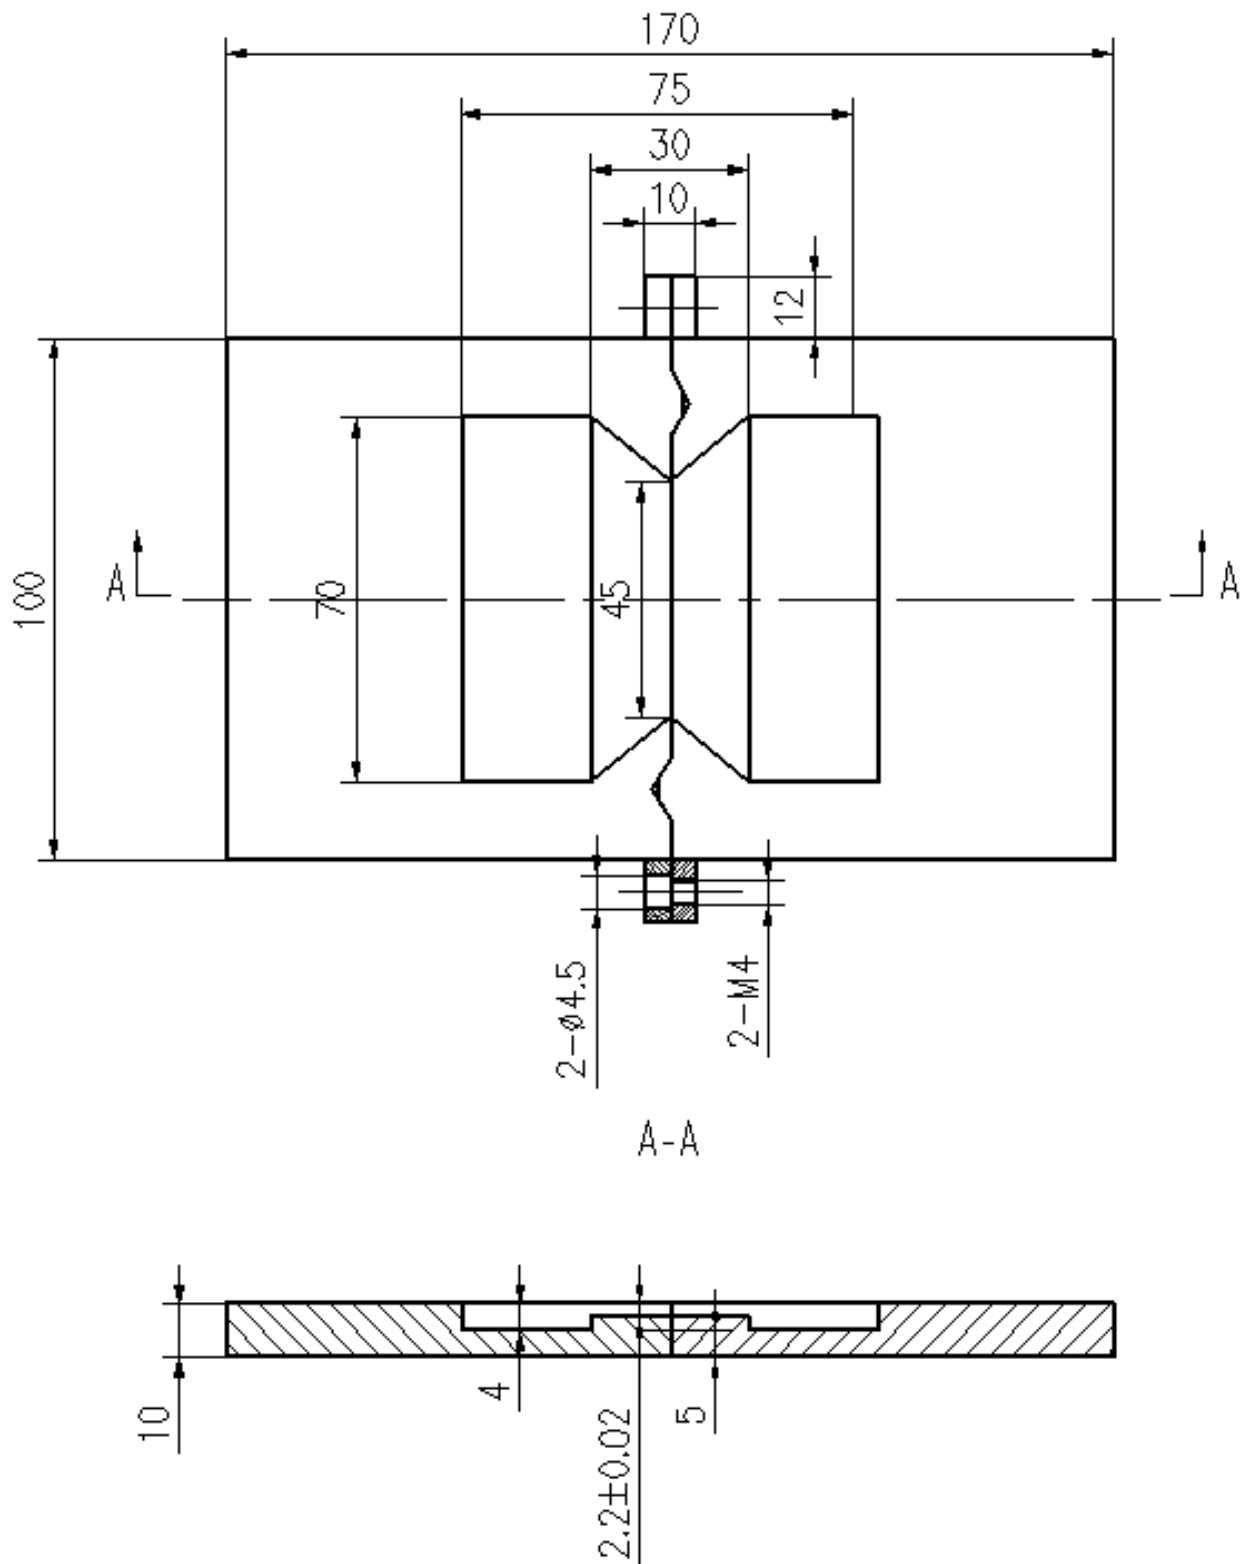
道路交通标线材料抗开裂性测试仪制样模具结构尺寸图
